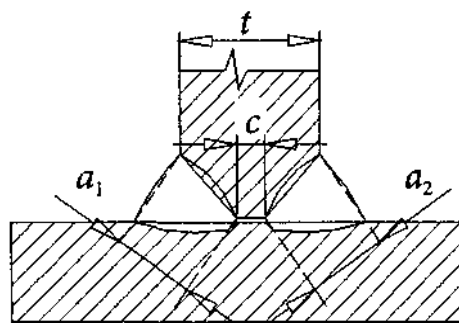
Шви зварювання Т-подібного рівномірного з'єднання з частковим проплавленням
